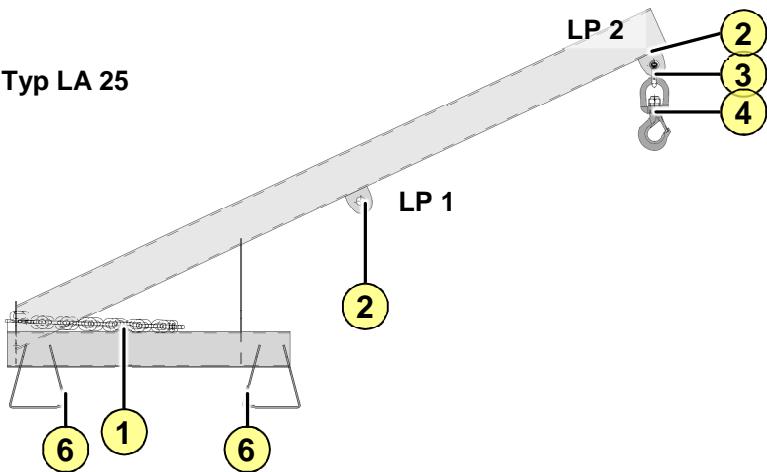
Baugruppen Lastarm LA 1600/2400-1,0/2,5/5,0 und LA 25-1,0
